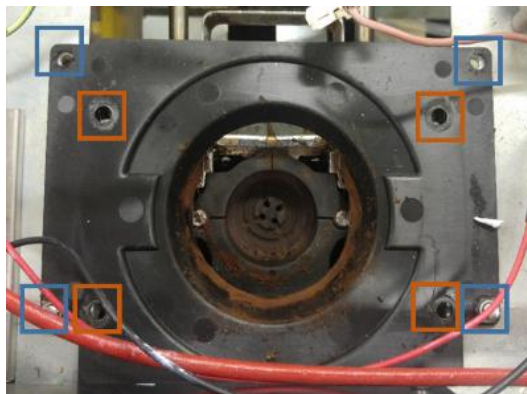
Placa de suporte em plástico com destaque, a laranja, os furos que alojam os parafusos que fixam o grupo à peça e os furos, a azul, que alojam os parafusos que fixam a placa ao corpo da máquina.
